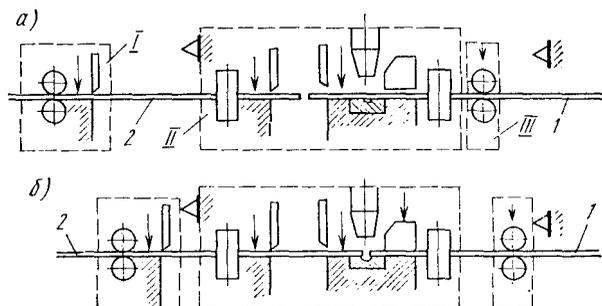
Схема летучего агрегата для сборки и сварки концов рулонов
